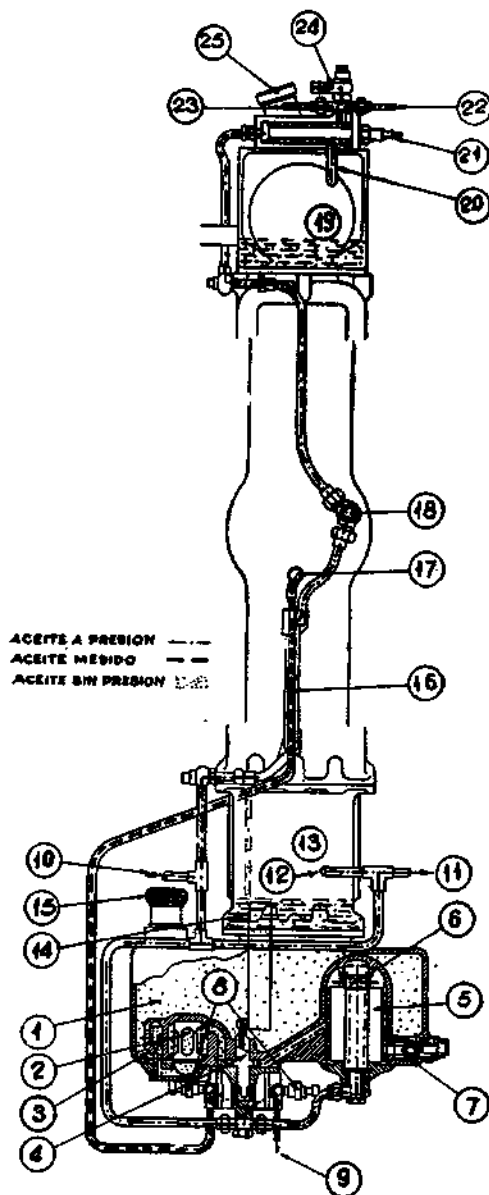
I.—Esquema del sistema de lubricación en el De Havilland Goblin II. (Del libro de instrucciones del De Havilland Technical Service.) 1, tanque; 2, filtro de aspiración; 3, válvula de drenaje del tanque; 4, bomba de engranajes; 5, filtro Tecalemit de presión; 6, válvula de sobrecarga; 7, válvula de regulación de la presión máxima; 8, bombas medidoras; 9, aceite medido para el cojinete posterior; 10, 11 y 12, aceite para accesorios; 13, cárter inferior de accesorios; 14, paso de aceite del cárter inferior de accesorios al tanque; 15, tapón del tanque, que deberá quitarse mientras se vierta el aceite desde la parte superior; 16, manguito anticongelante del aceite medido; 17, aceite medido para el cojinete delantero; 18, chorro de aceite para los engranajes centrales; 19, cárter superior de accesorios; 20, chorro de aceite al cárter de accesorios; 21, conexión para termómetro; 22 y 23, aceite para los accesorios; 24, conexión para manómetro; 25, tapón superior por donde se vierte el aceite.
